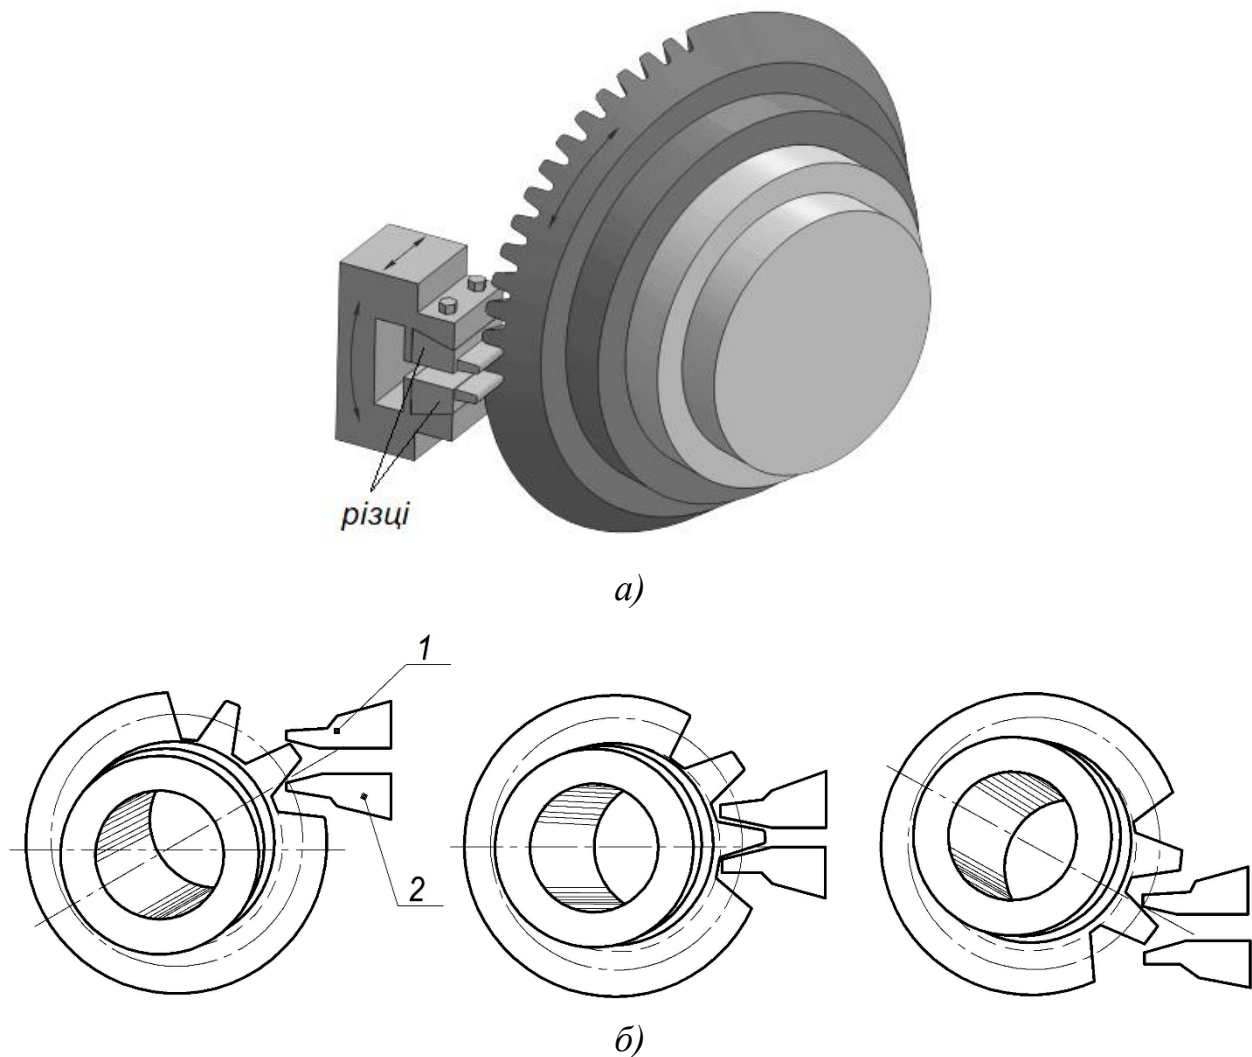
Нарізування конічного зубчастого колеса на зубостругальному верстаті:
